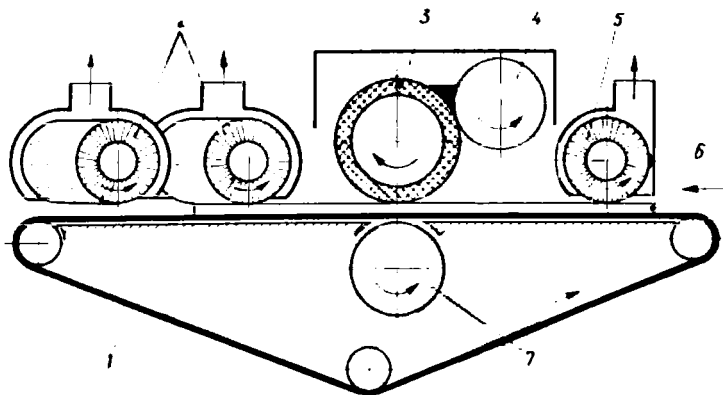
Схема станка для крашения щитов КЩ9-1:
